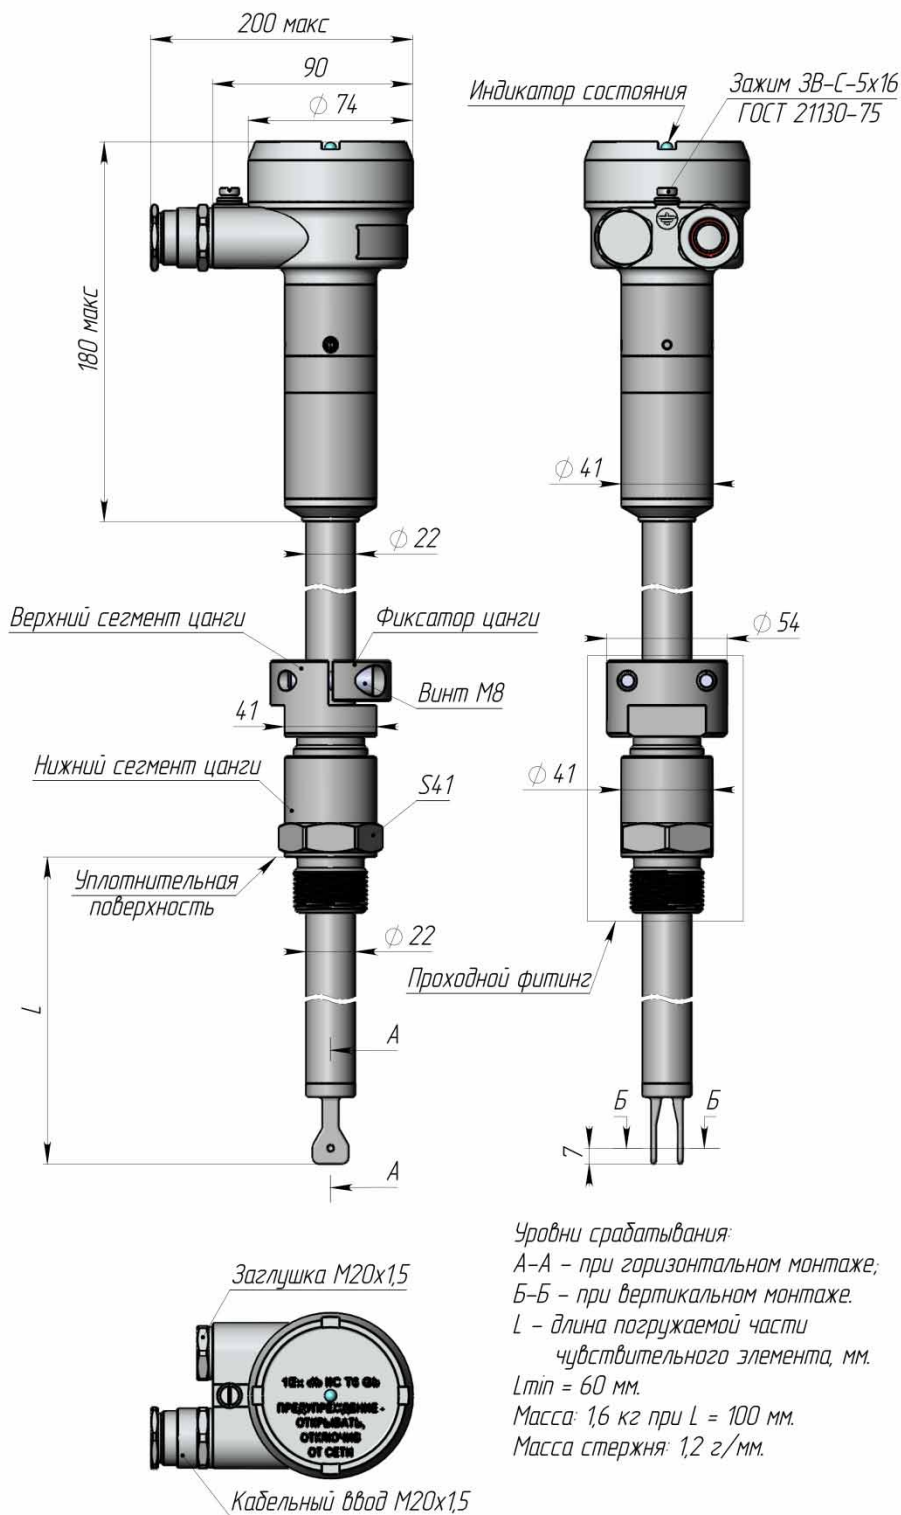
Габаритные и установочные размеры сигнализатора уровня ВИБРОТЭК-У-М-В с изменяемой высотой контролируемой среды (проходным фитингом). Способ присоединения - штуцер
